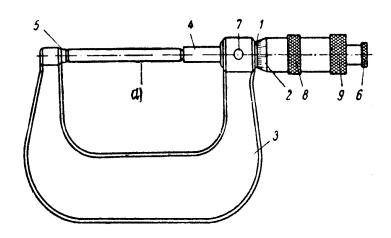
Микрометр с пределами измерений 25—50 мм: 1 — стебель; 2 — барабан; 3 — скоба; 4 — микровинт; 5 — неподвижная пятка; 6 — трещотка; 7 — стопорный винт; 8 и 9 — накатные выступы
